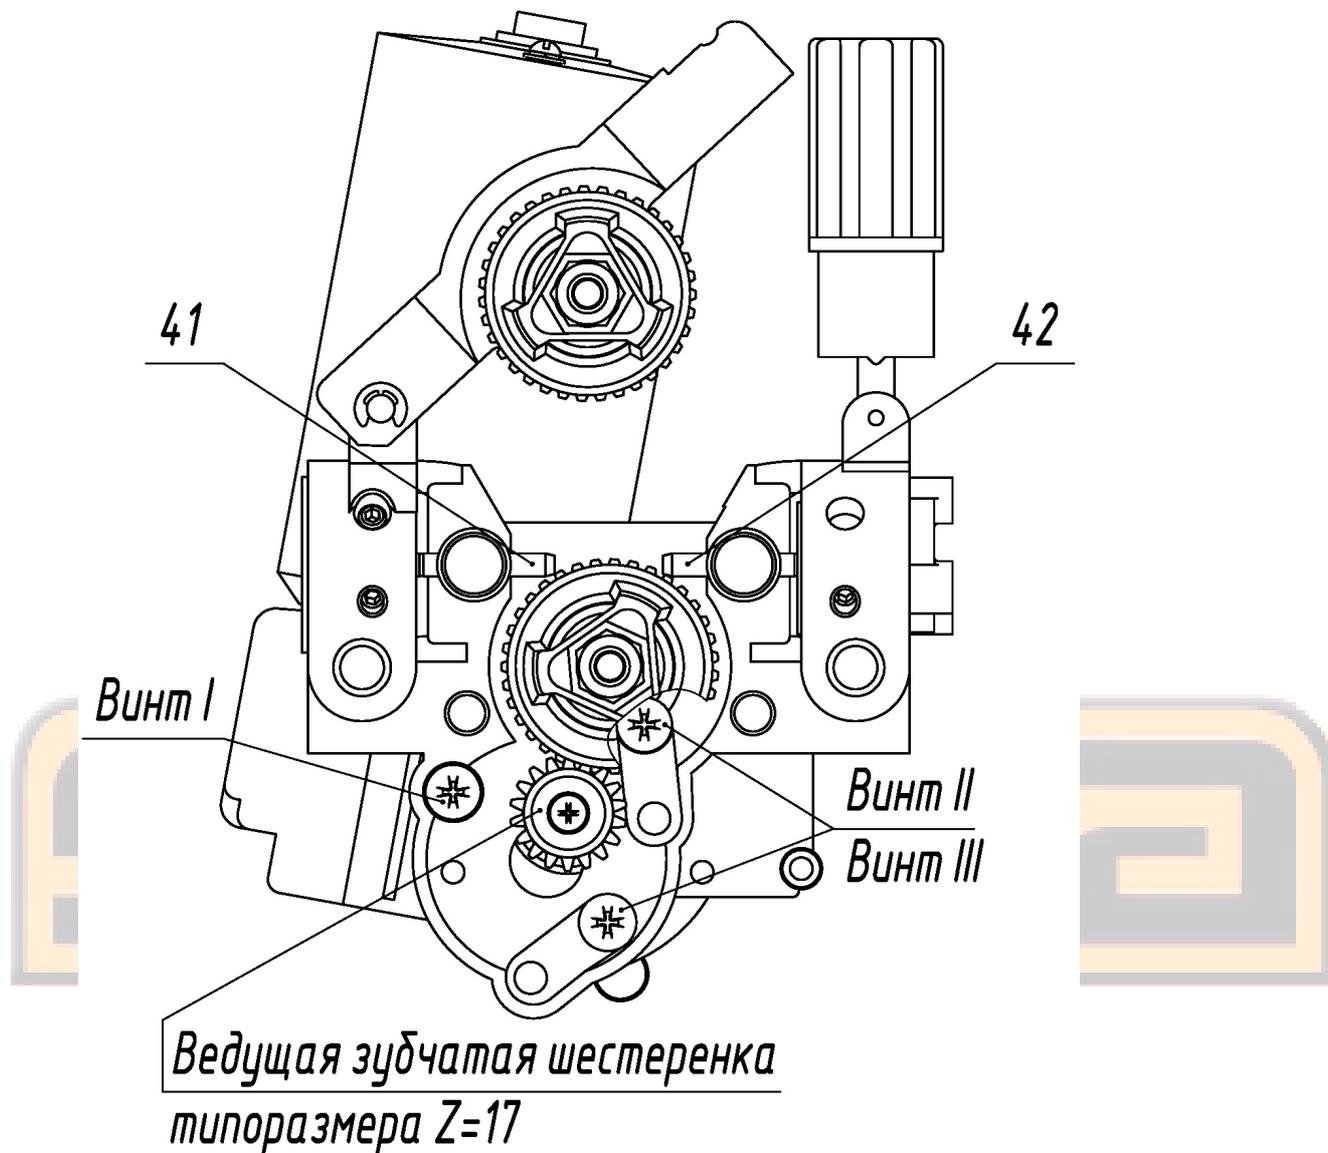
Механизм подачи проволоки SSJ-21 с установленной ведущей зубчатой шестеренкой типоразмера $Z=17$
